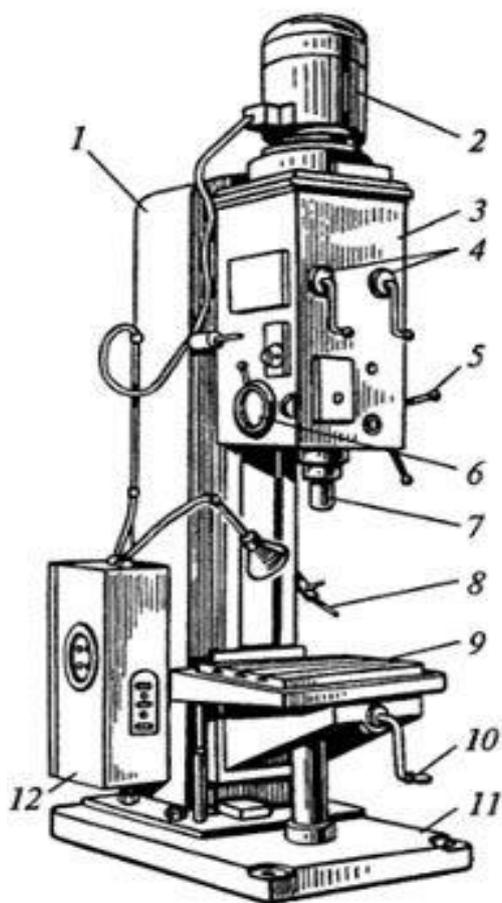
Вертикально-сверлильный станок модели 2Н125
